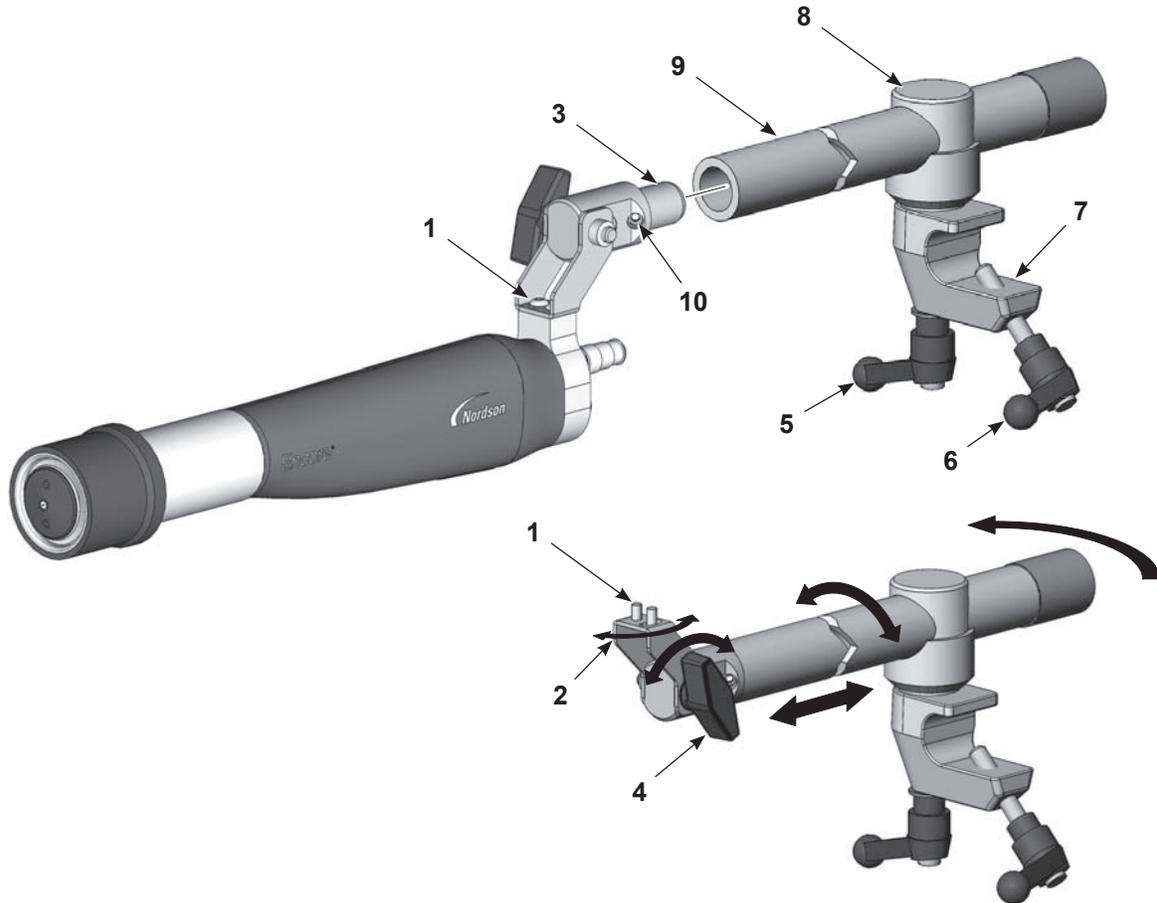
Montaje de la pistola de montaje en barra articulada estándar
